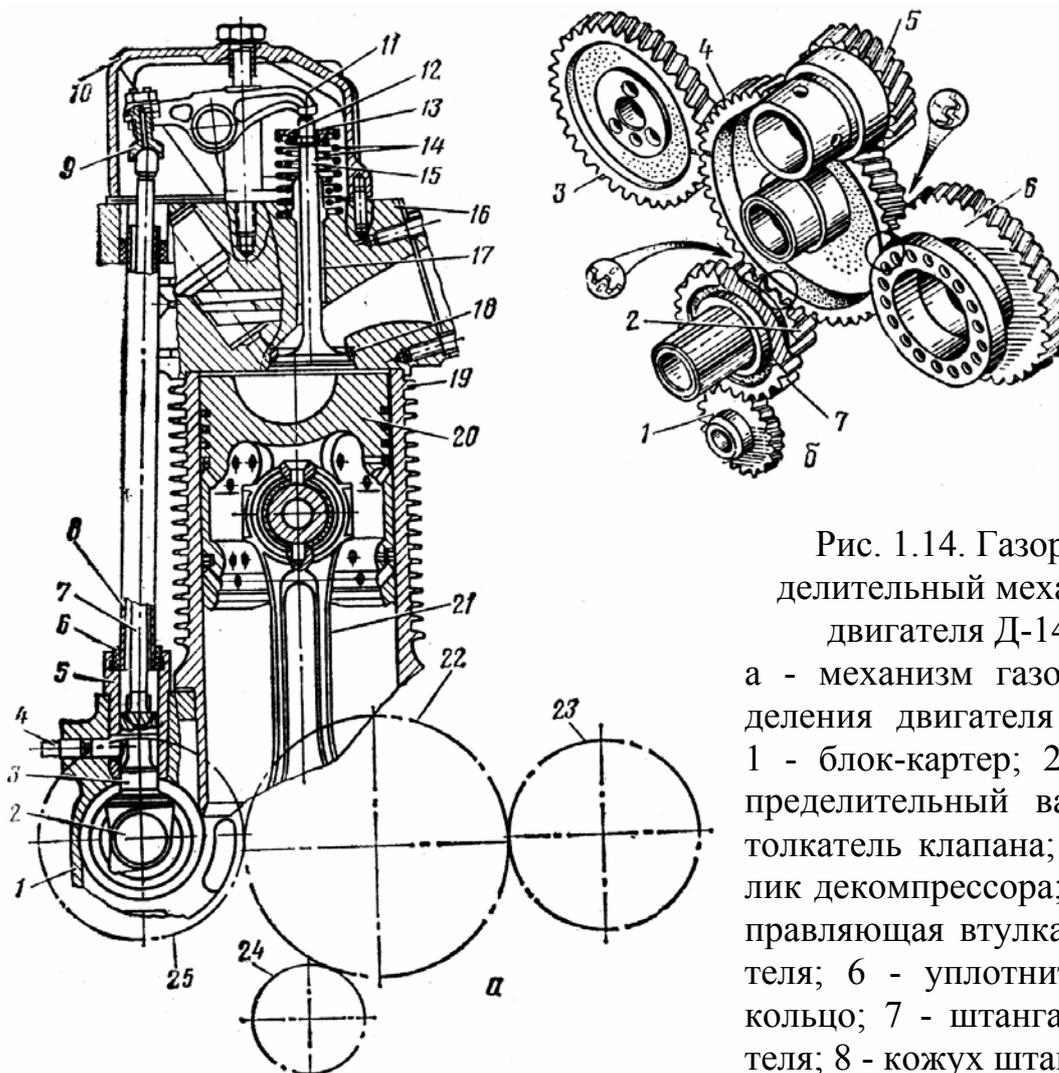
Газораспределительный механизм двигателя Д-144:
